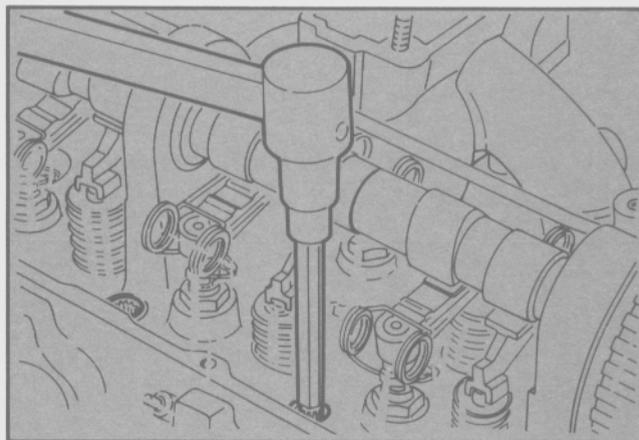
Herramienta T84G-6065-BAS para tornillos de tapa de cilindros
